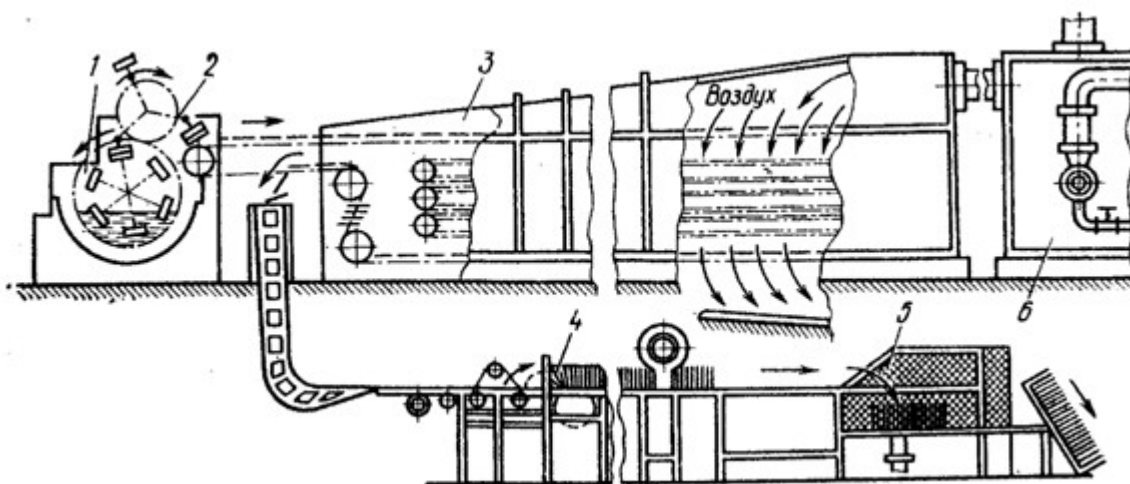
Схема установки для изготовления прокладок из бумажного литья: 1 – установка для формования прокладок; 2 – пересъемное устройство; 3 – сушильная камера; 4 – счетное устройство; 5 – узел упаковки; 6 – воздухоподогреватель
